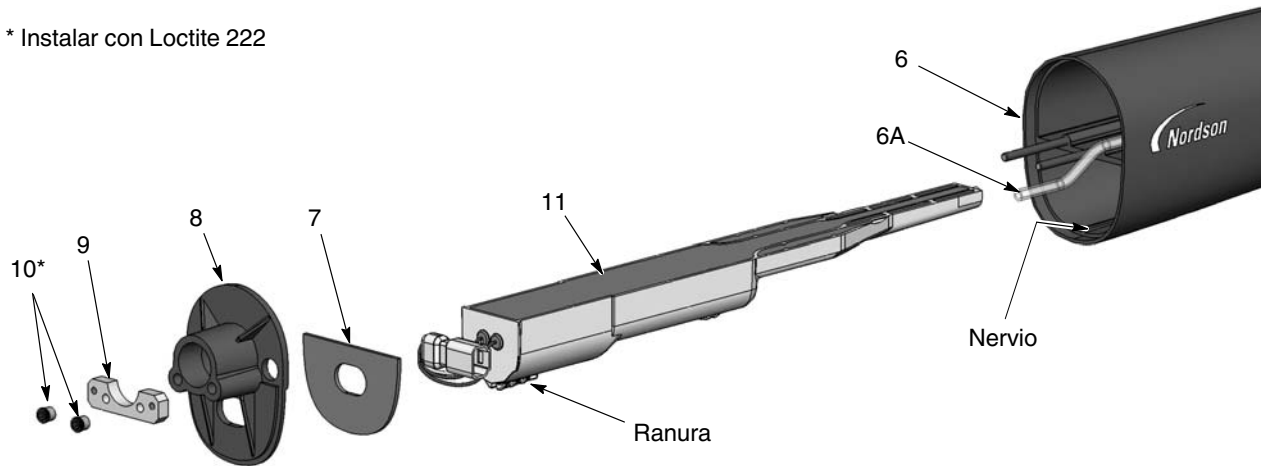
Desmontaje de la pistola de montaje en barra 2 de 3
